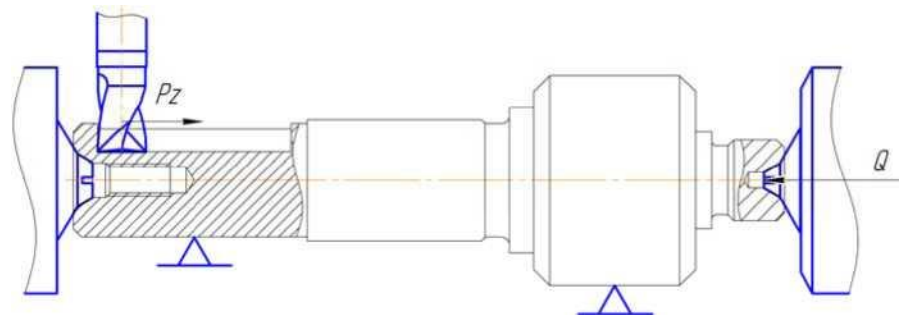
Розрахункова схема сил, що діють при фрезеруванні на 025 шпонково-фрезерній операції
